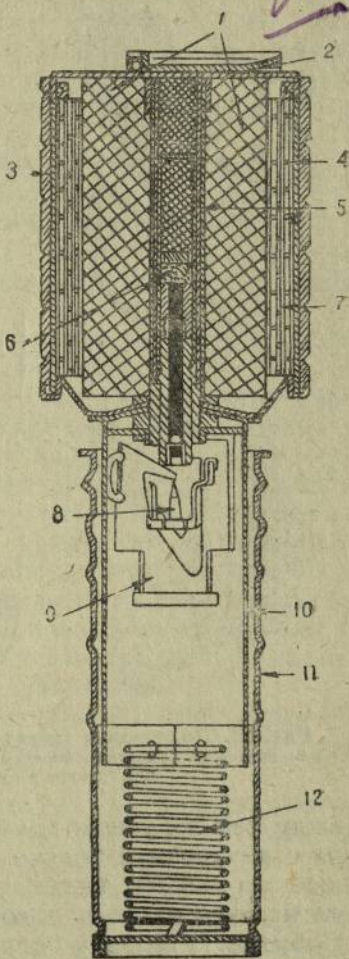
Ручная граната образца 1933 г. в разрезе.
